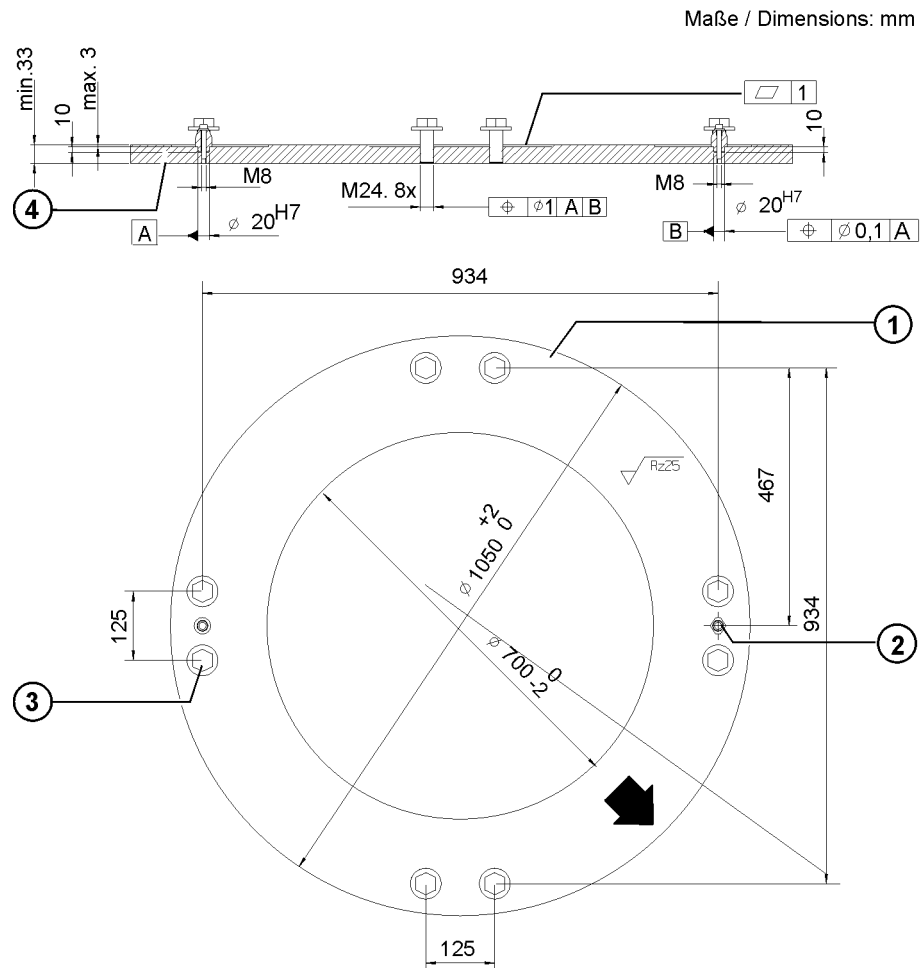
Maschinengestellbefestigung, Maßzeichnung
